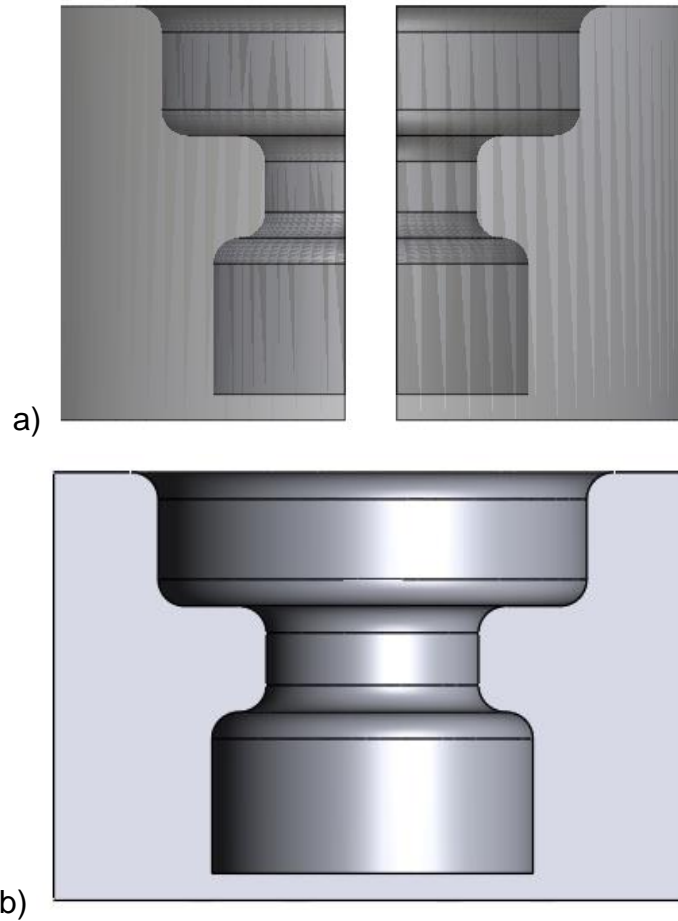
a) Imagen del CAD del soporte de la pieza 7 tras haber realizado el corte del mismo para facilitar su retirada; b) Imagen del CAD de una de las 2 partes que forman el soporte empleado para la fabricación de la pieza 7.
